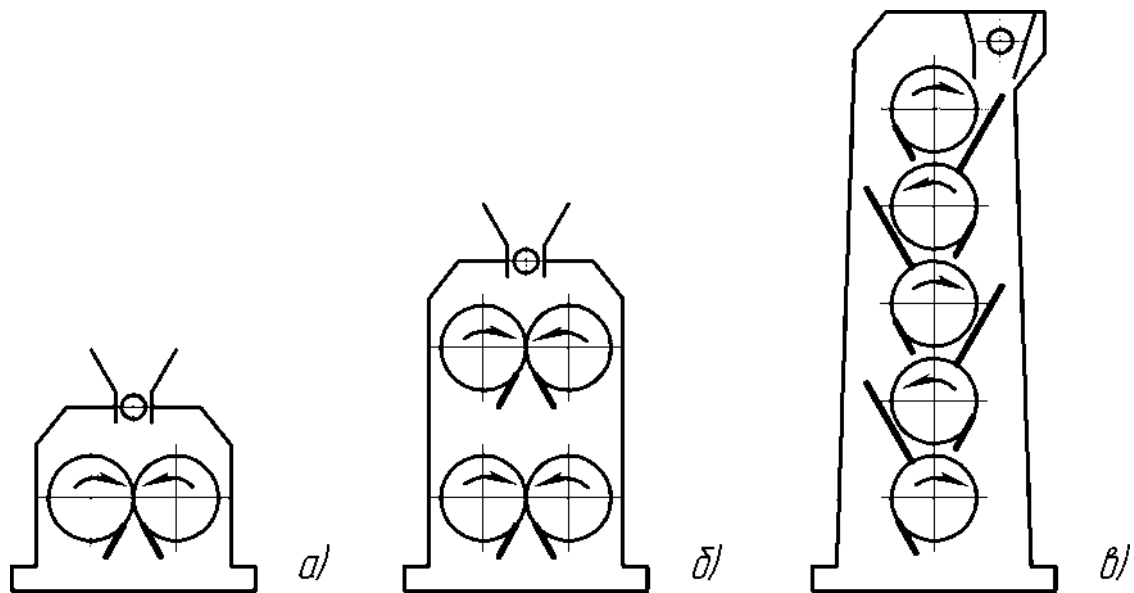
Схеми конструкцій вальцьових верстатів
